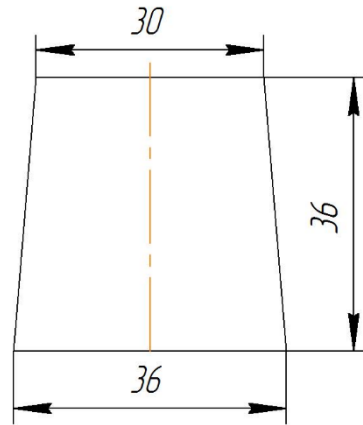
Эскиз сечения шлакоуловителя
